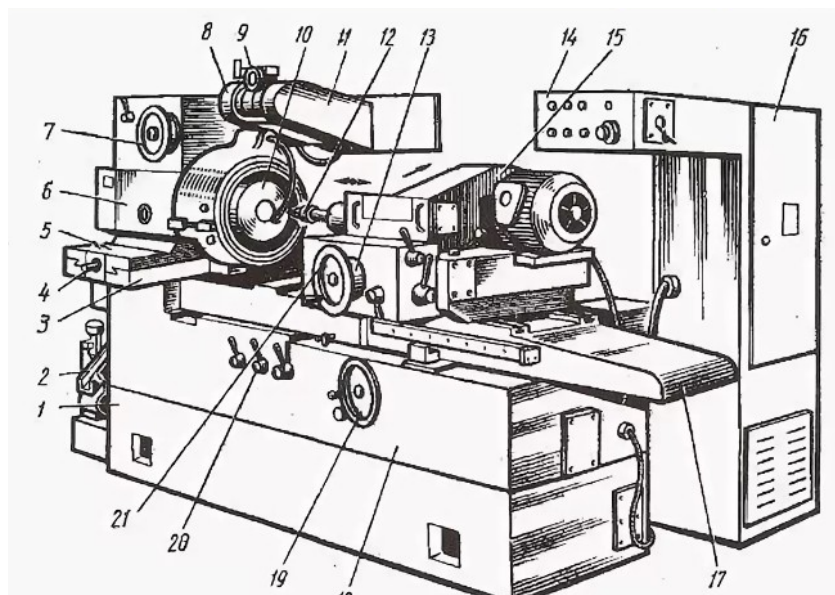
ЗК228А станок внутришлифовальный универсальный
